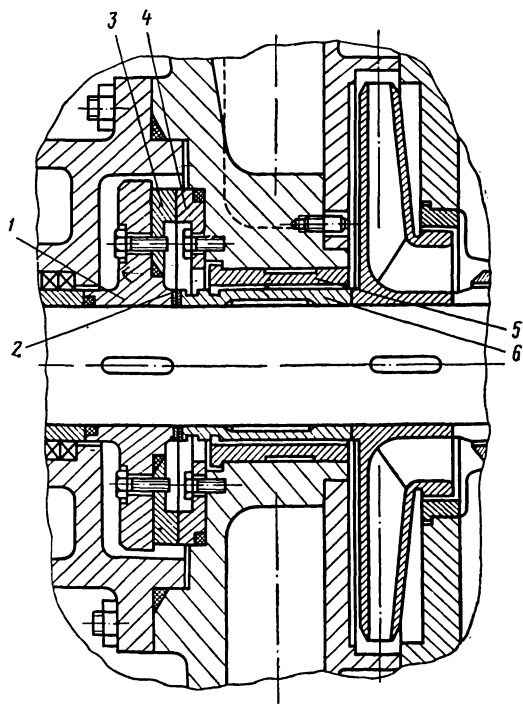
Разгрузочное устройство насосов ЦНС 180-85...425 и ЦНС 300-120...600
